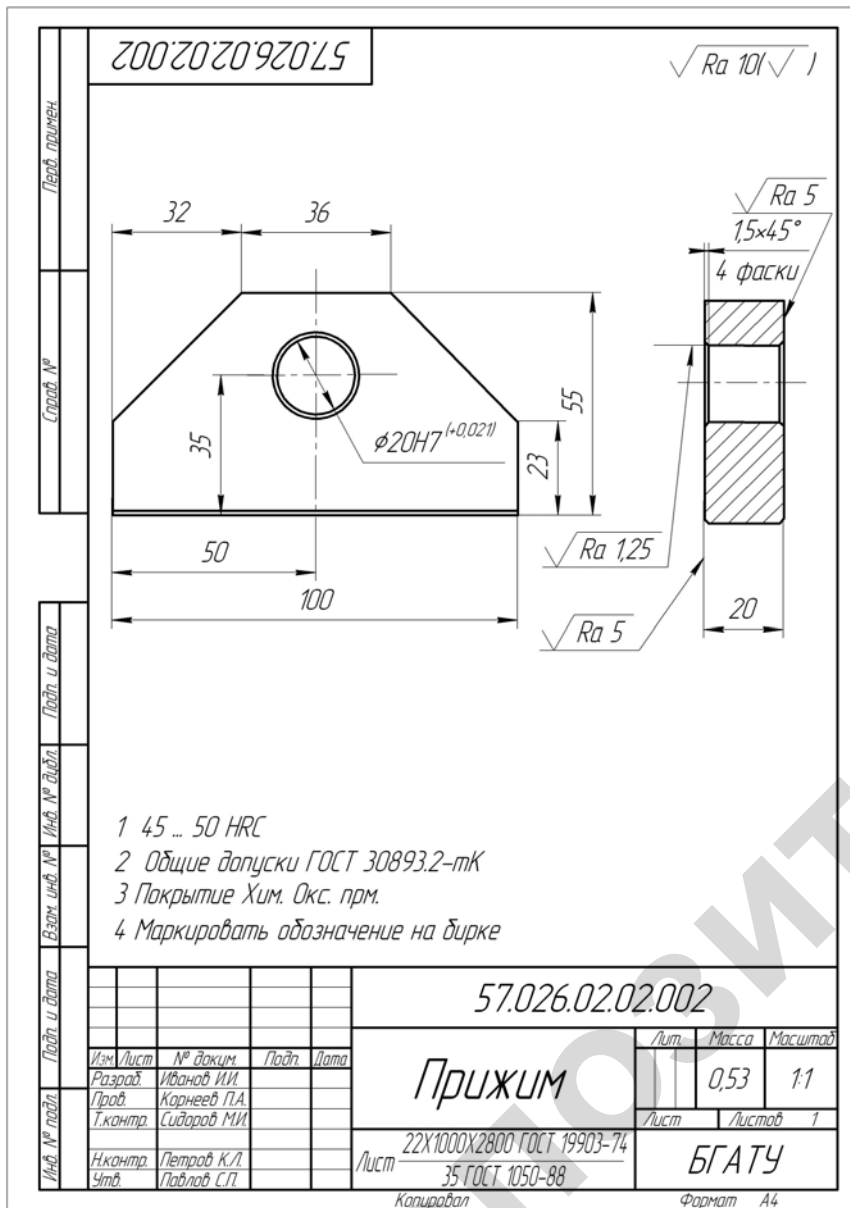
Чертеж детали с цифровым обозначением основных и дополнительных поверхностей
